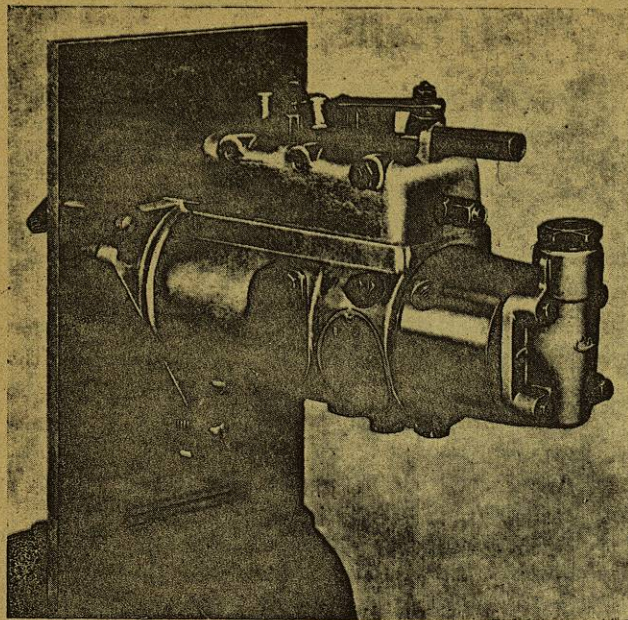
Bomba con regulador mecánico montada sobre dispositivo para su montaje y desmontaje
